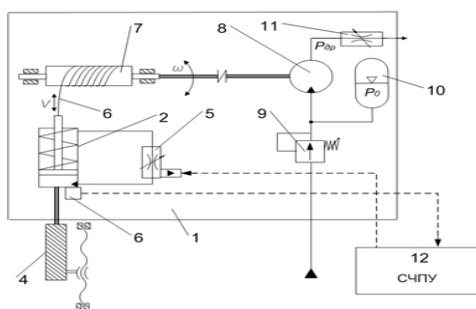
Кинематическая схема виброгасителя подвижного узла станка
